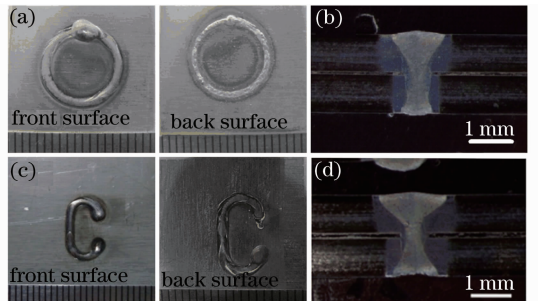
环形和 C 形激光焊缝典型表面及截面形貌。(a) 环形焊缝表面；(b) 环形截面；(c) C 形焊缝表面；(d) C 形截面
